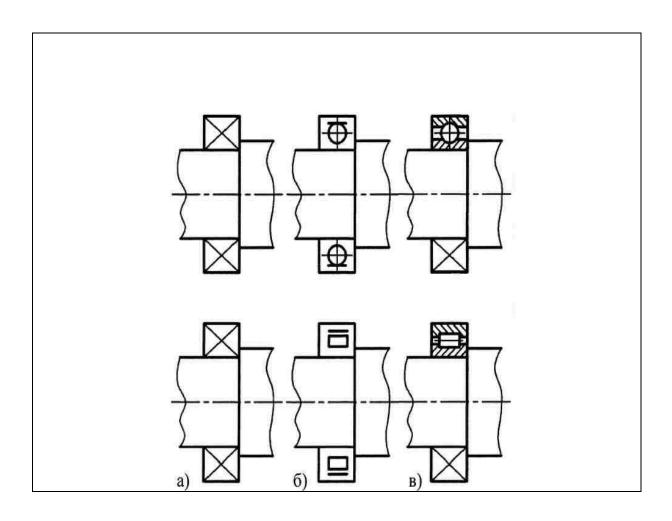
Примеры изображения подшипников качения в разрезах на сборочных чертежах: а - упрощенное без указания типа подшипника; б - условное с указанием типа; в-допускаемое
